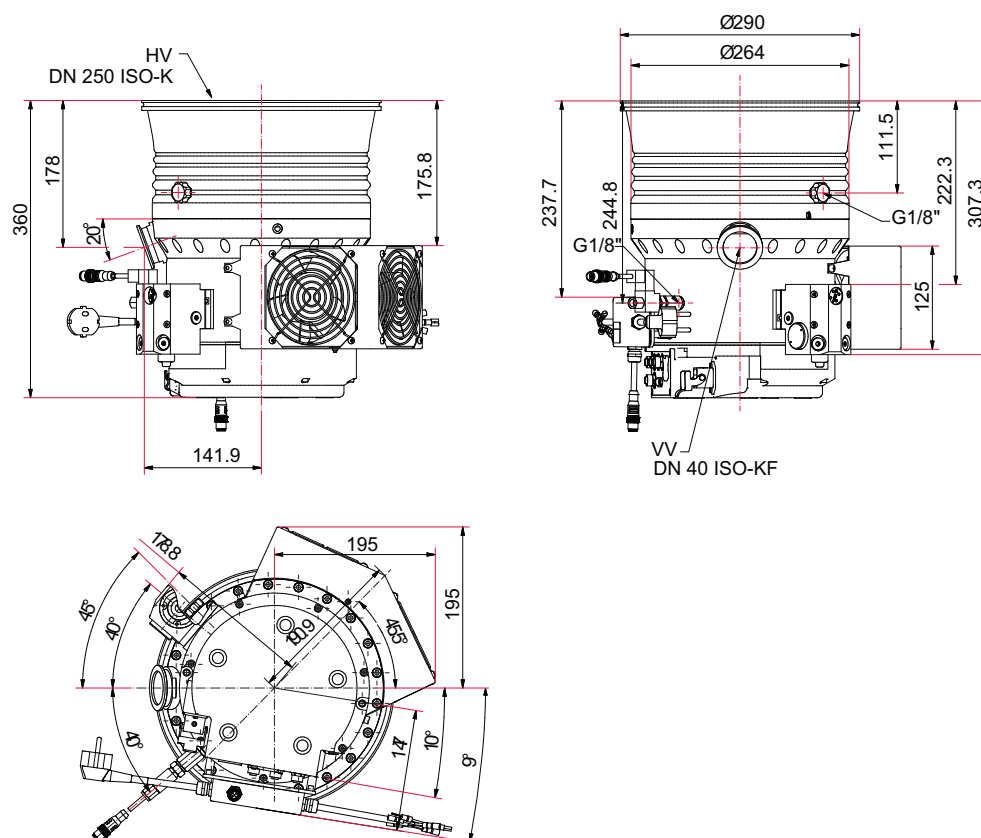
Dimensions de la HiPace 1500 C | DN 250 ISO- K
